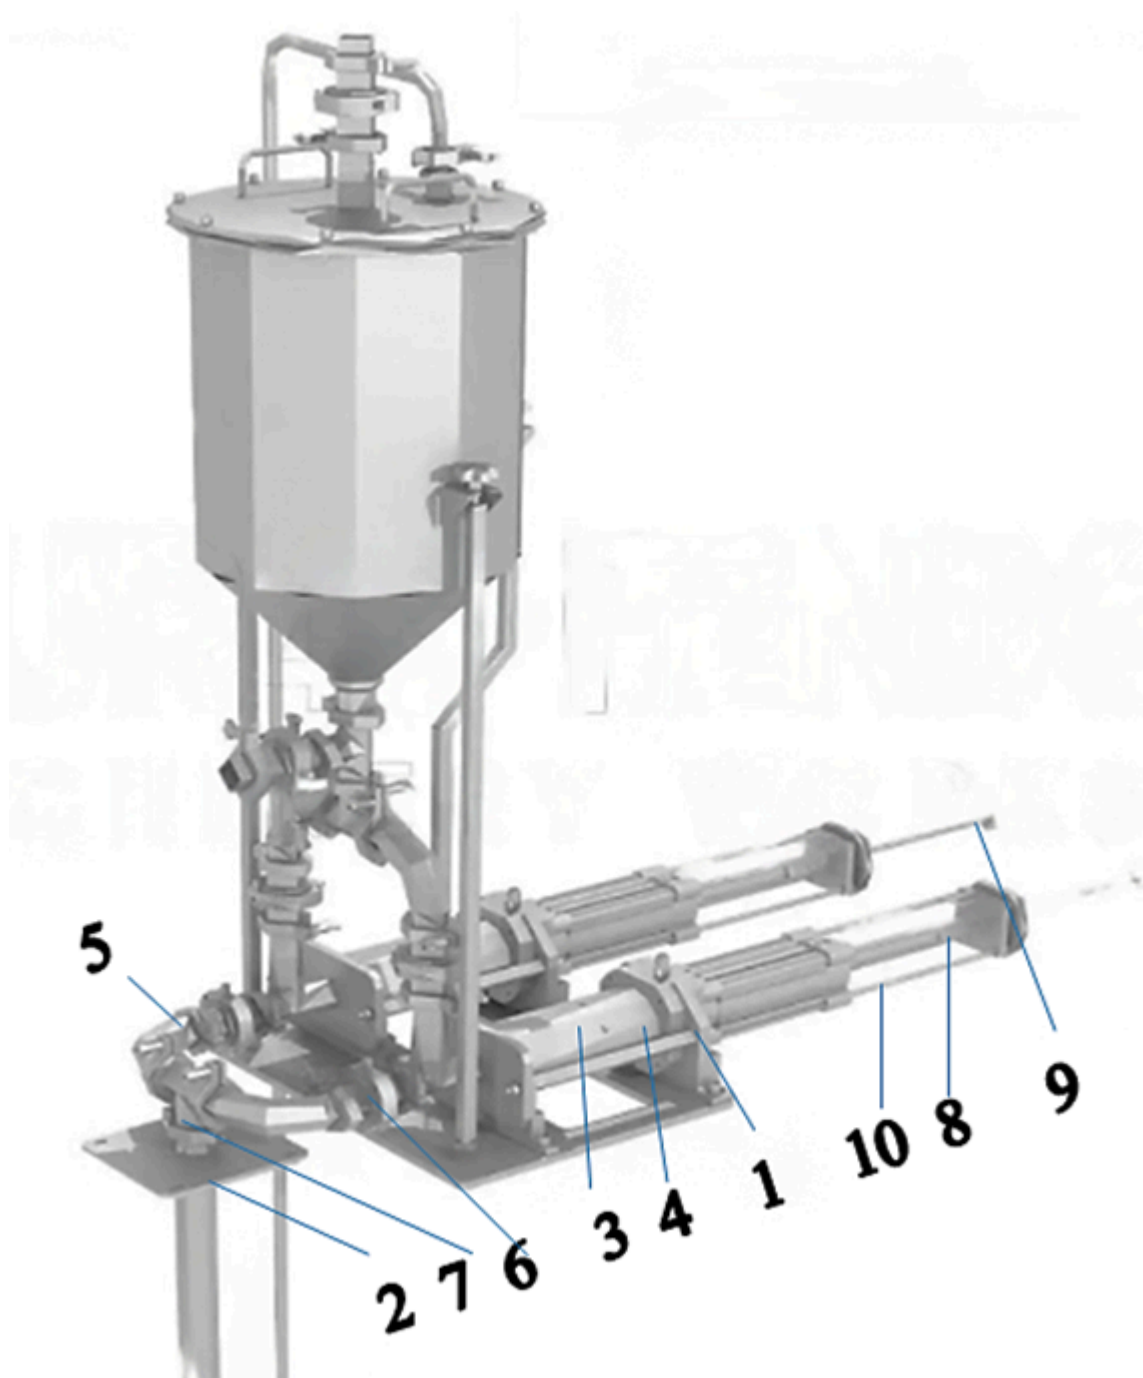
Дозуючий пристрій з поршнем механізмом: 1- рама; 2 - фланець; 3 – порожнина вимірювання дози; 4 - поршень дозатора; 5 – привід пневматичний; 6 - клапан; 7 - золотник; 8 - пневматичний циліндр; 9 – регулювальний пристрій; 10 – опора
